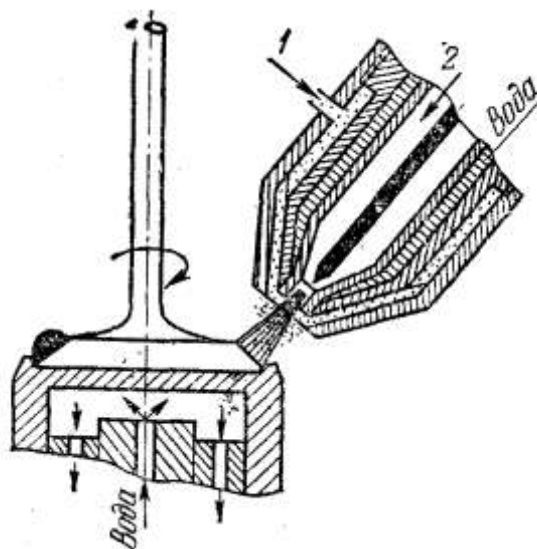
Схема плазменной наплавки рабочей фаски клапана:
